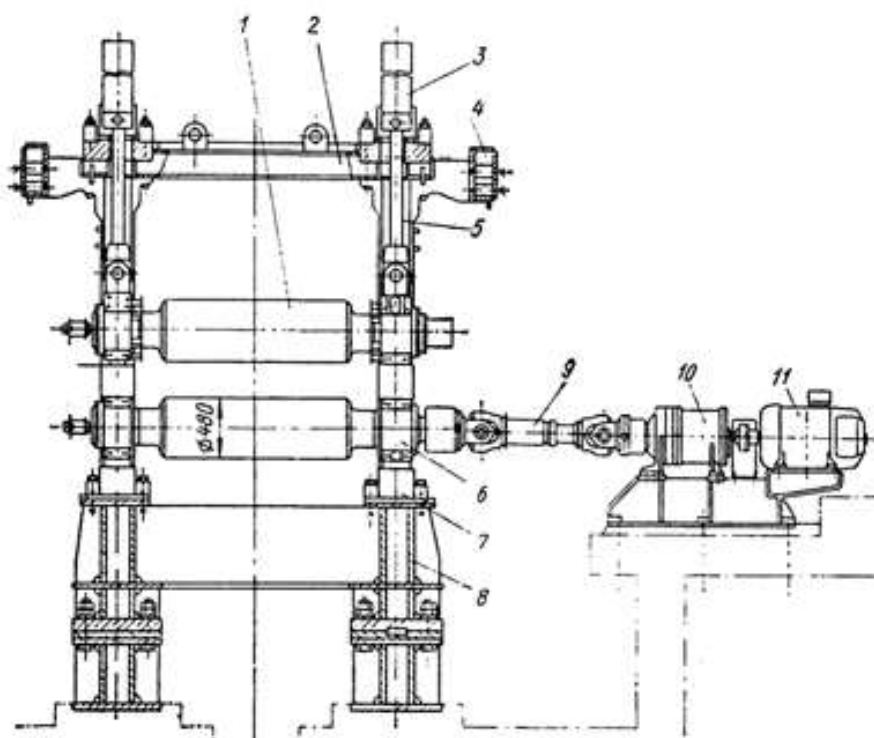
Поперечный разрез тянуще-правильной машины: 1 – верхний неприводной ролик; 2 – поперечные связи; 3 – гидроцилиндры перемещения и прижатия роликов; 4 – продольные балки; 5 – стойки; 6 – нижний ролик; 7 – опорные гидроцилиндры; 8 – станина; 9 – шпиндель с шарнирами Гука; 10 – планетарный редуктор; 11 – электродвигатель.
